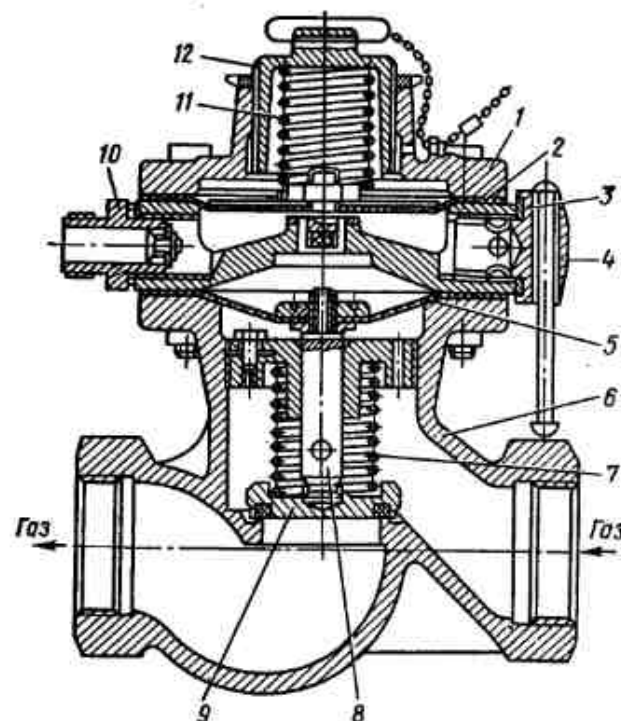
Запорно-предохранительный клапан ПКК-40М:
